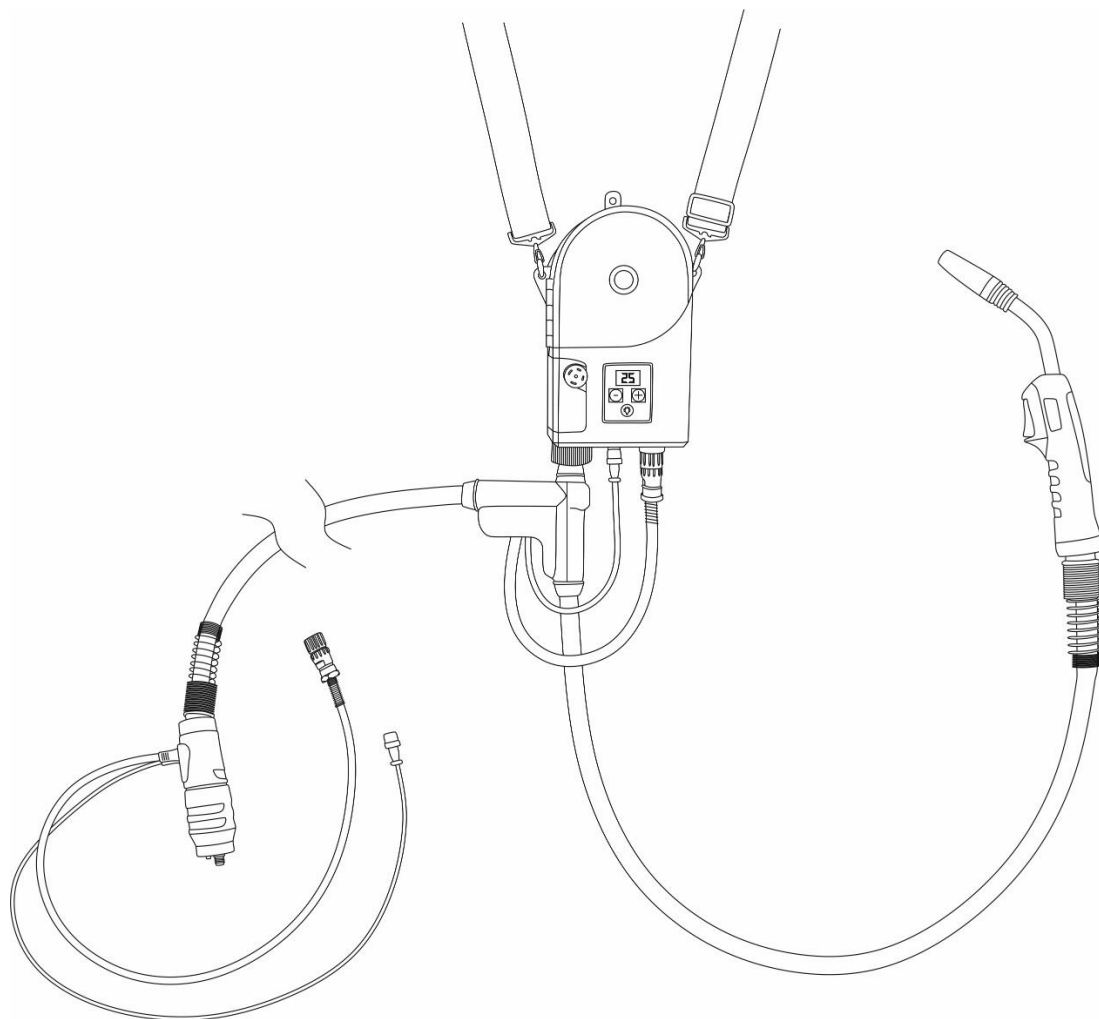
Подключение удлинителя горелки для MIG/MAG сварки.
